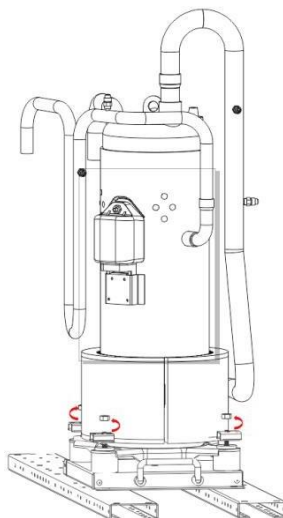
Снятие крепежных деталей компрессора из листового металла
